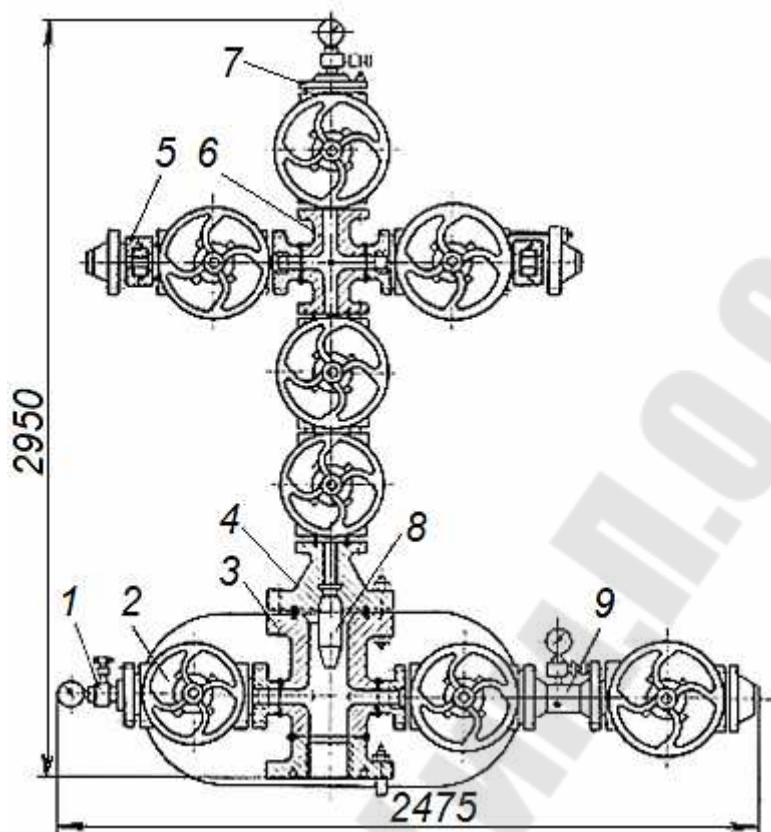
Фонтанная крестовая арматура (4АФК-50-700) высокого давления (70 МПа) для однорядного подъемника: 1 – вентиль, 2 – задвижка, 3 – крестовина, 4 – катушка для подвески НКТ, 5 – штуцер, 6 – крестовина фонтанной ёлки, 7 – буфер, 8 – патрубок для подвески НКТ, 9 – катушка
